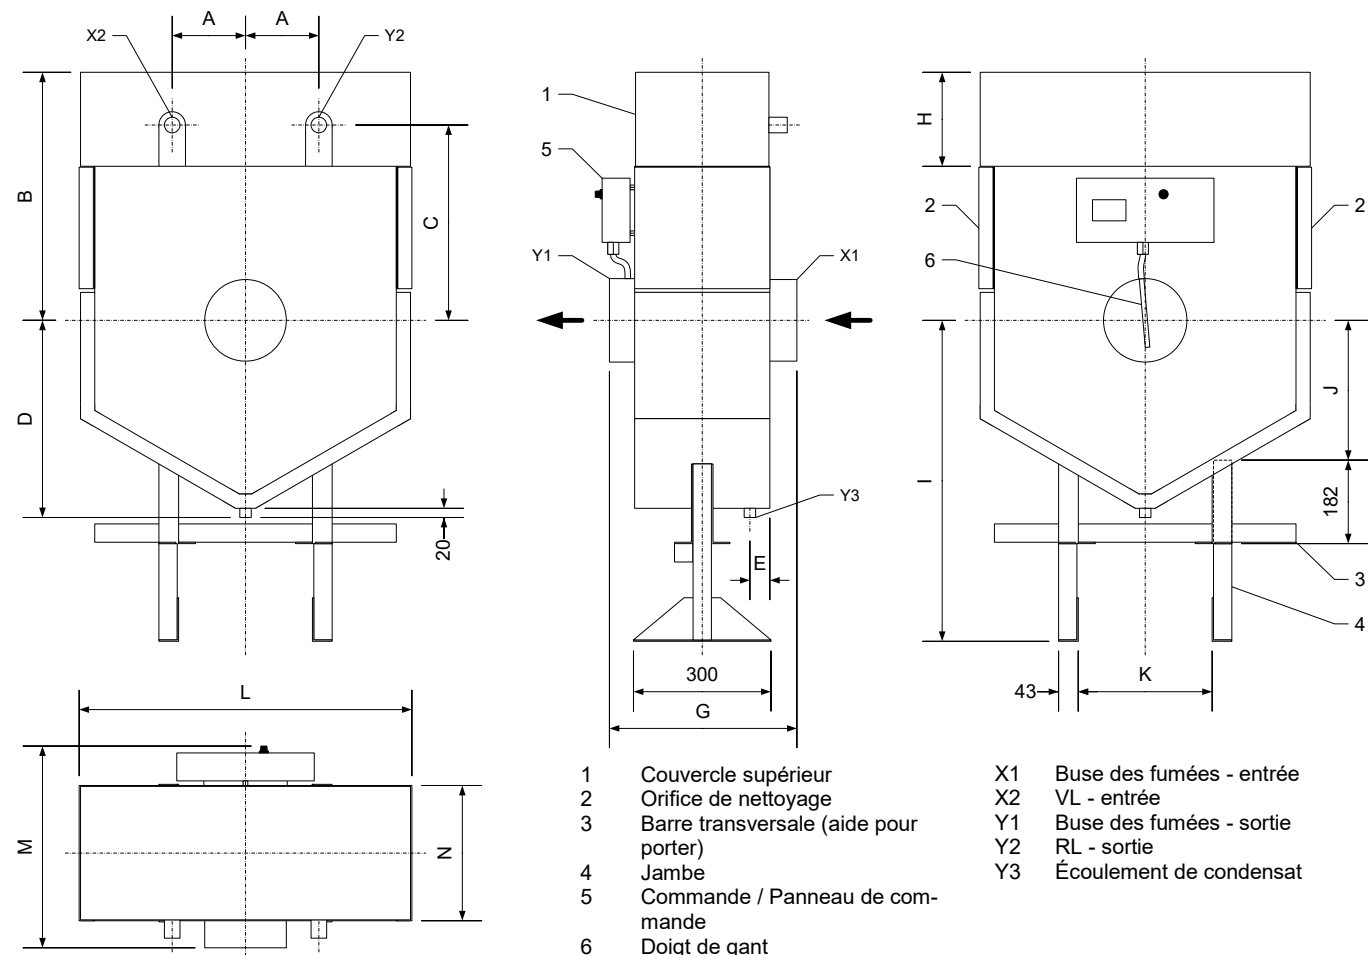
Dimensions MX 90 - 250 (330 - 650)
